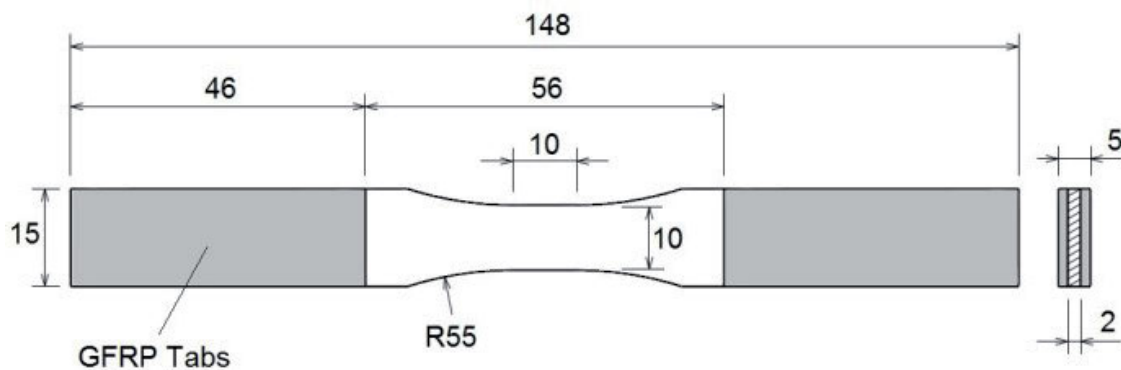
Dimensiones y diseño de las probetas de ensayo. Fuente: [16]
